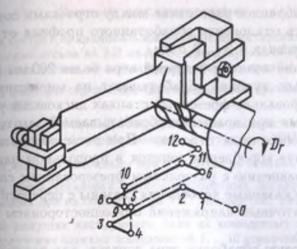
Схема фрезерования пера лопатки на станке с ЧПУ
